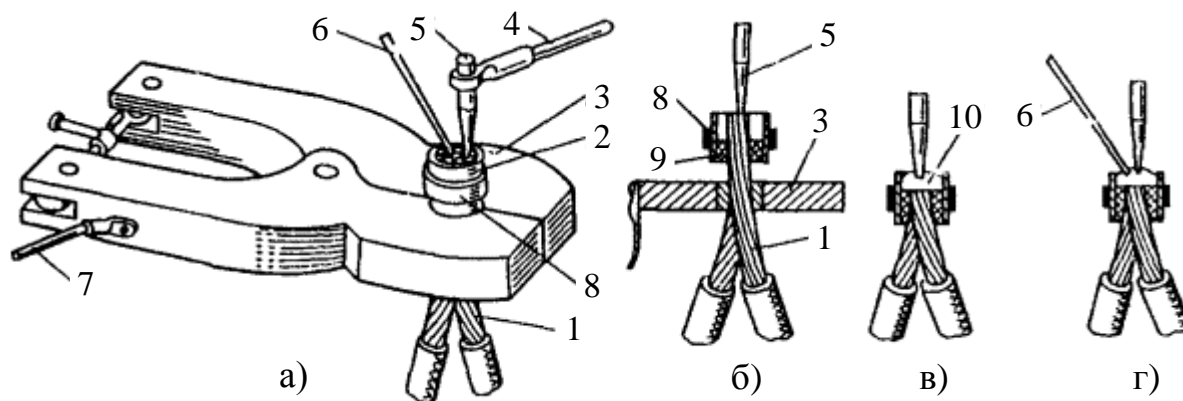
Сварка алюминиевых жил сплавлением в общий монолитный пучок.
